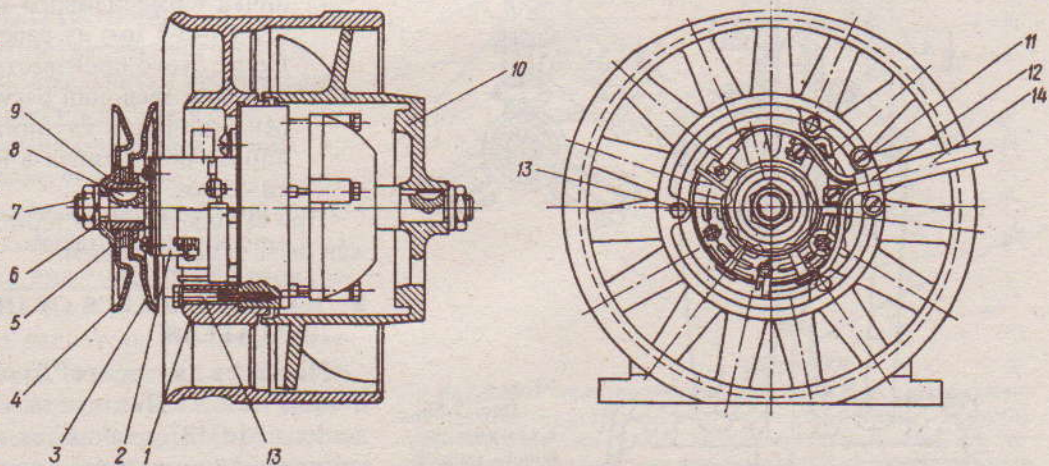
Вентилятор с генератором в сборе: 1 - направляющий аппарат; 2 - генератор в сборе; 3 - задняя половина шкива; 4 - передняя половина шкива; 5 - шайба регулировочная; 6 - шайба пружинная; 7 - гайка; 8 - шпонка 4x6,3; 9 - нажимной колпачок; 10 - колесо вентилятора; 11 - винт M5x10; 12 - скобка крепления проводов; 13 - болт генератора к направляющему аппарату; 14 - провода от генератора к реле-регулятору
